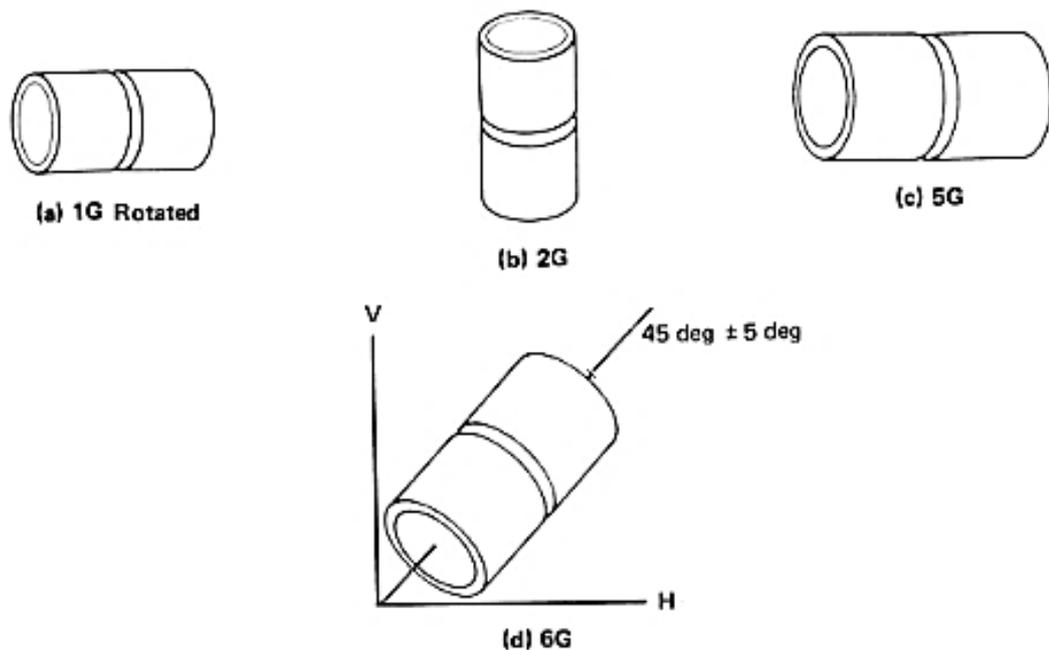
Posiciones de soldadura para tubería en ranura.
